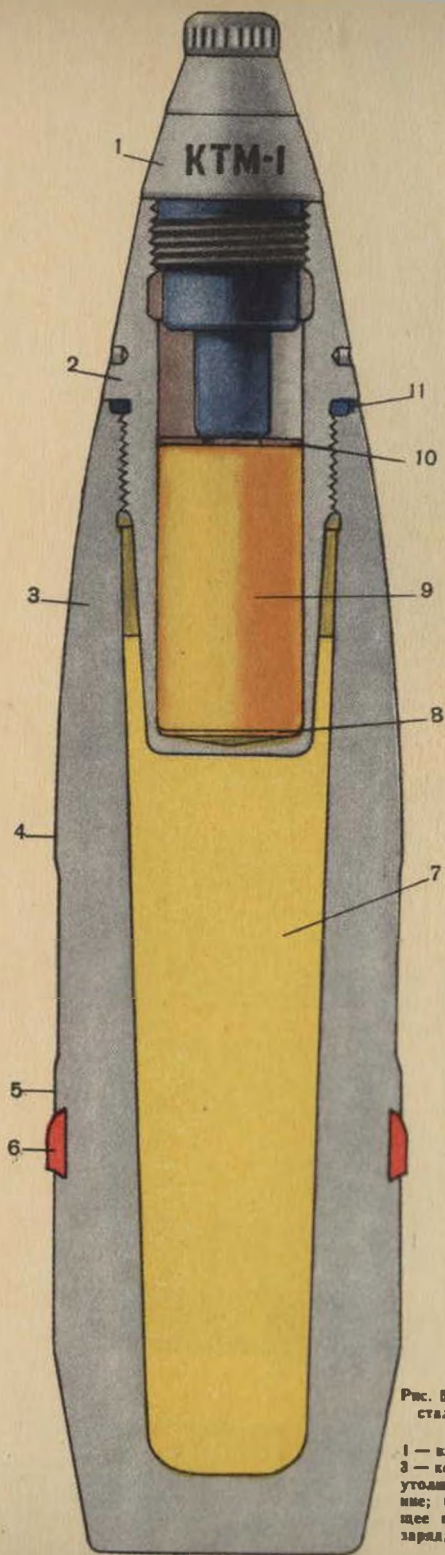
76-мм дымовой дальнобойный снаряд стальной чугуна Д-350А со взрывателем КТМ-1 (в разрезе):
